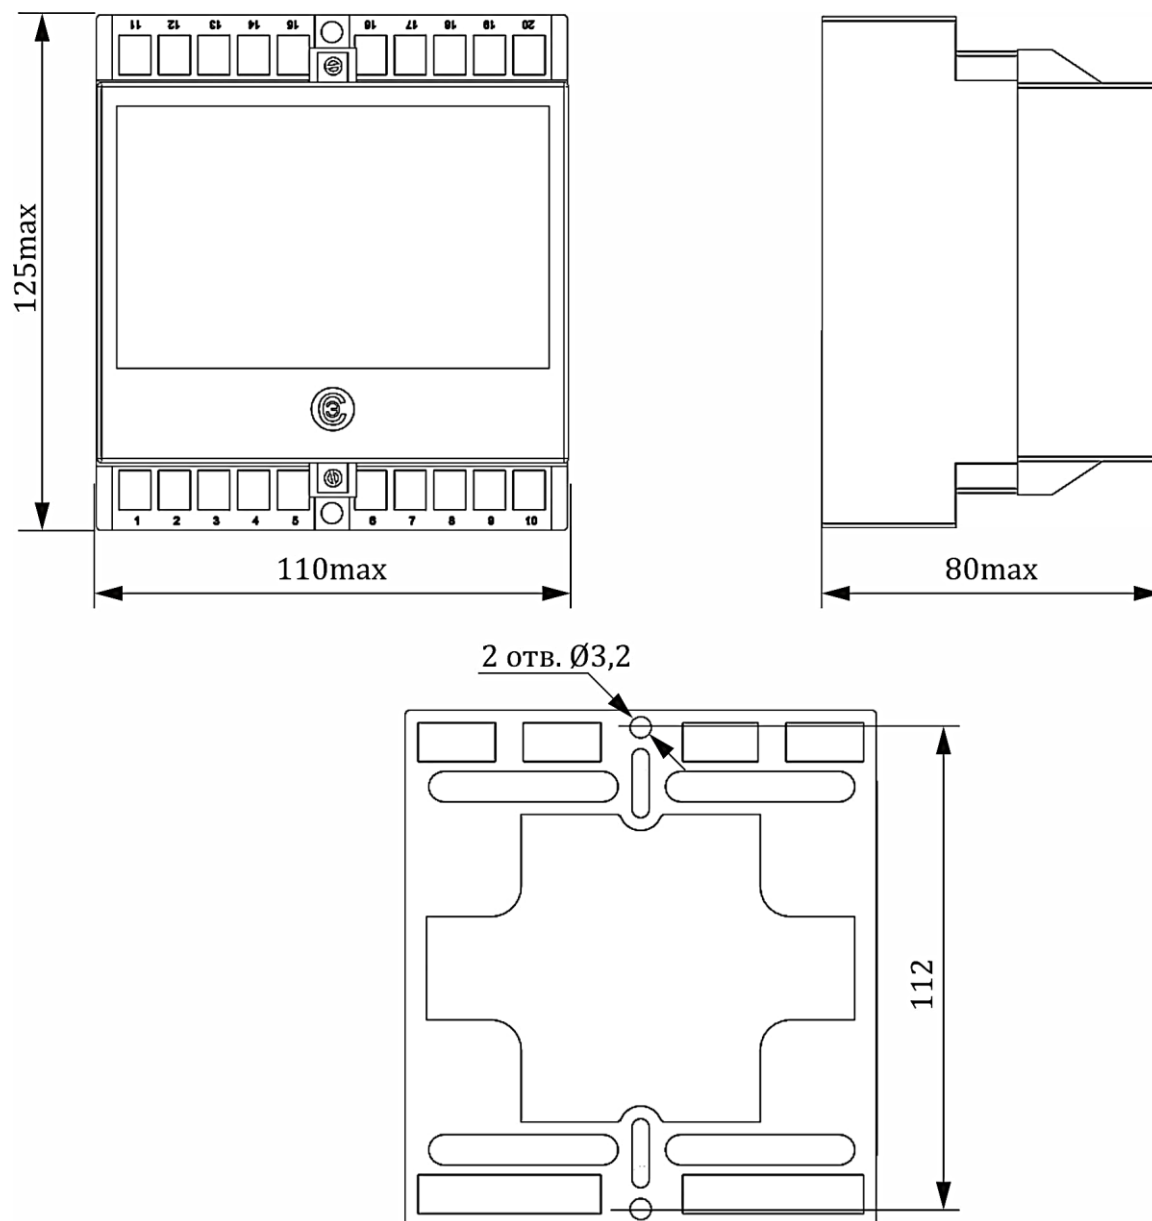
Габаритные и установочные размеры корпуса E20
